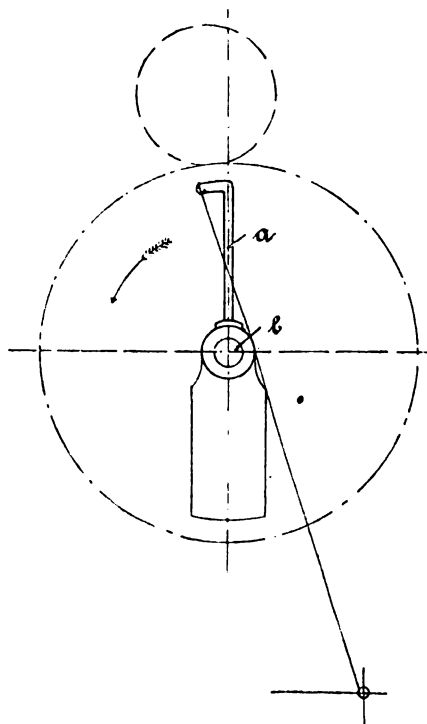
Disposizione per la guida del filo della "Herm. Schroers Maschinenfabrik" di Krefeld.
